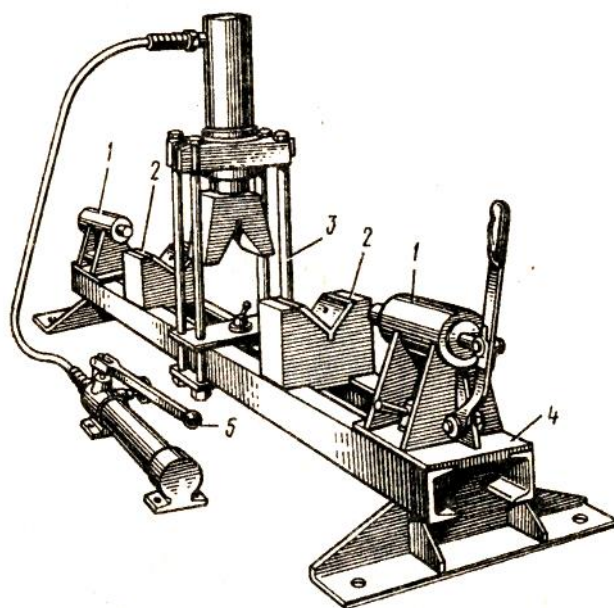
Схема стенда модели 684 для проверки и правки карданных валов:
